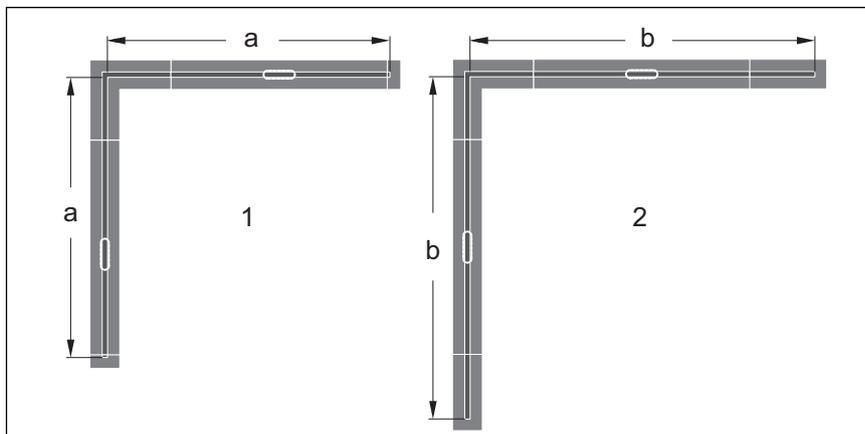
Opciones de montaje con piezas de unión de 90° para variante en L
